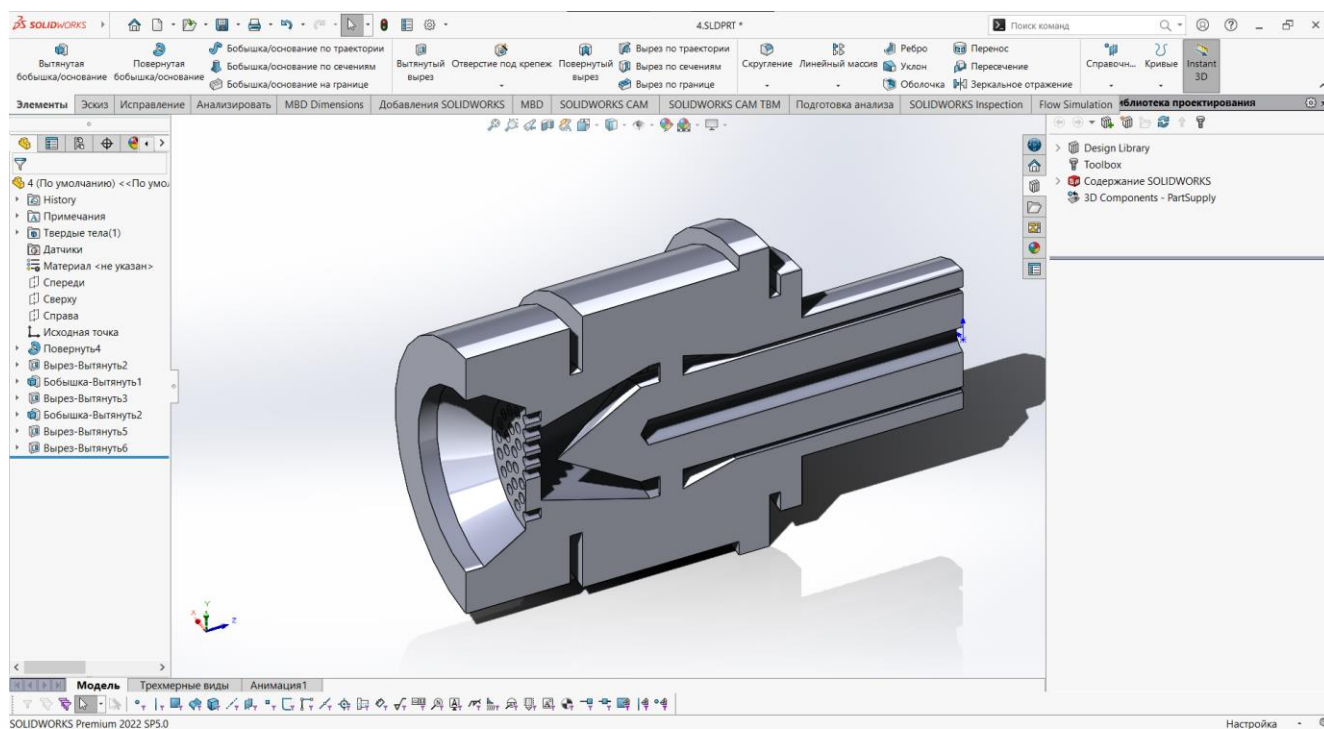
3D-модель базовой конструкции формующей головки в разрезе
